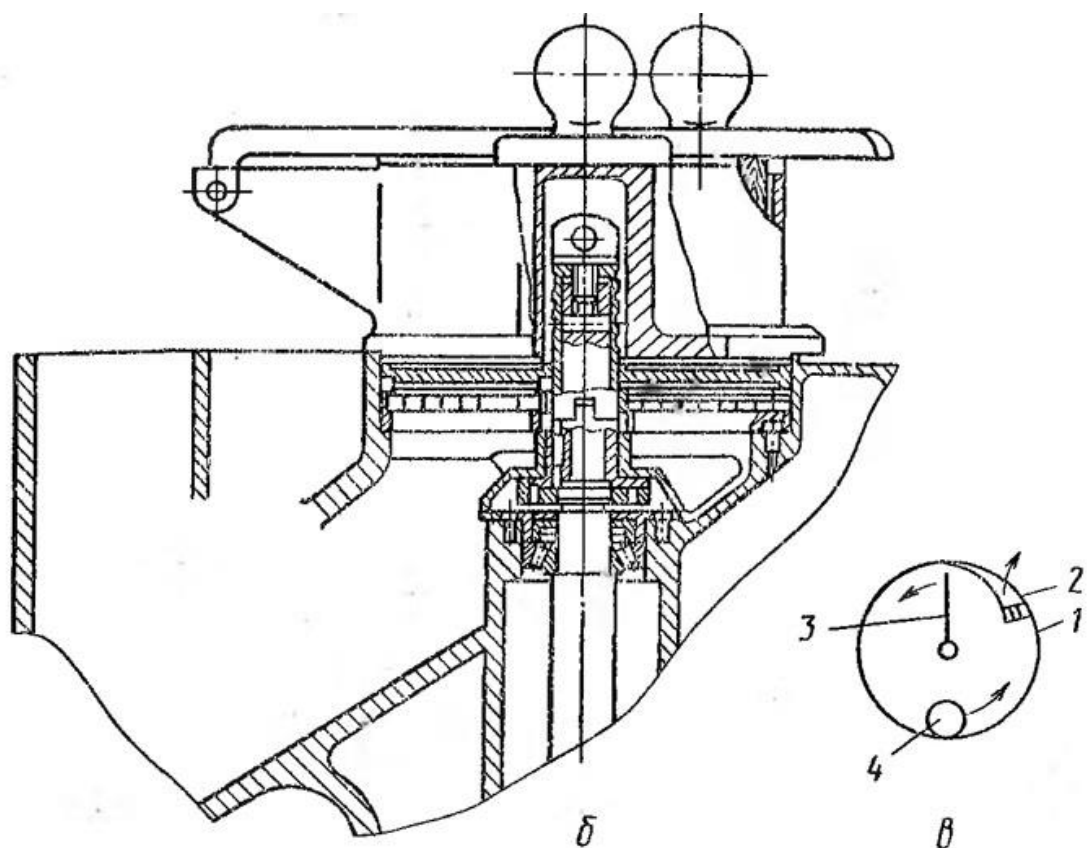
б,в – Машина овощерезательная МРО-400-1000: а – общий вид (разрез): 1 – приводной вал; 2 – регулировочная гайка; 3 – стакан; 4 – канал для выгрузки продуктов; 5 – ножевой блок; 6 – стопорный винт; 7 – загрузочная воронка; 8 – лопасти ротора; 9 – ротор; 10 – барабан; 11 – электродвигатель; 12 – клиноременная передача; 13 – фиксирующая защелка; 14 – зацеп; б – ручное приспособление; в – схема резароторной машины: 4 – рабочая камера; 2 – ножевой блок; 3 – ротор; 4 – продукт.
